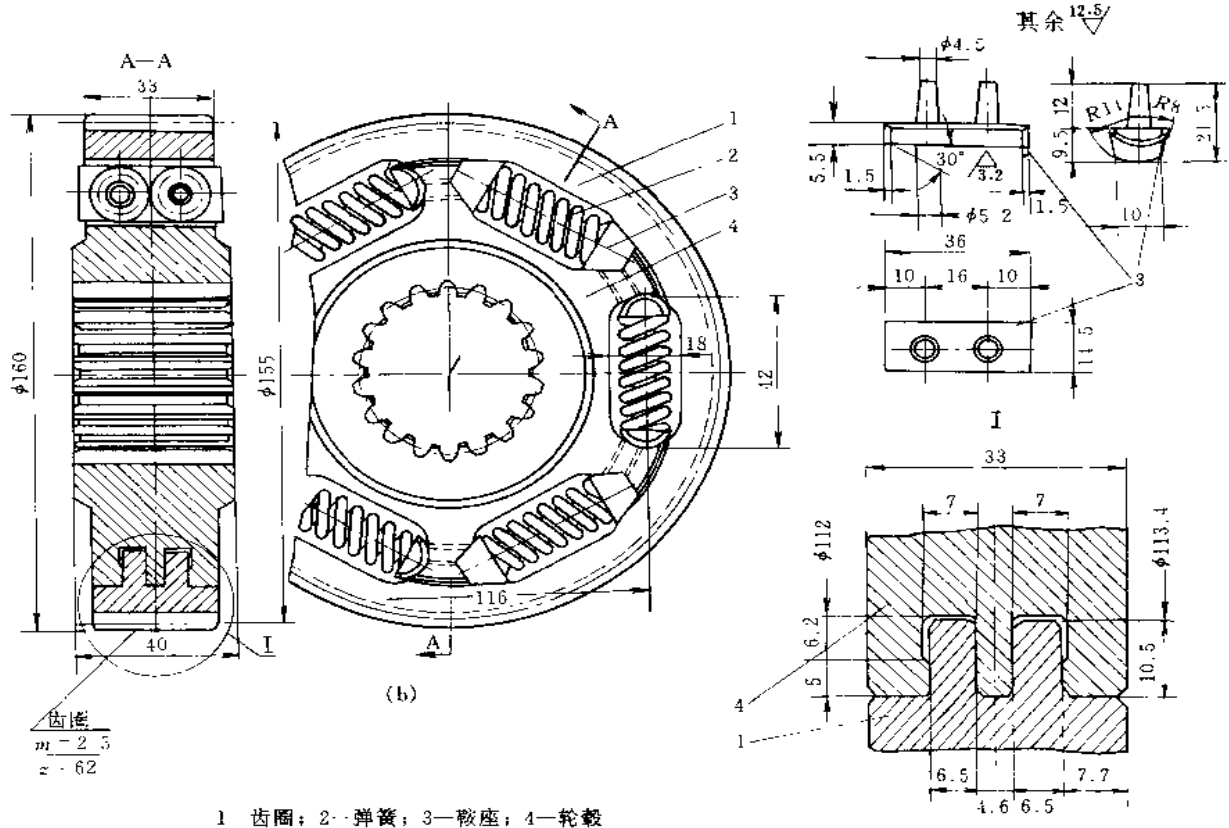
具有弹性元件的齿轮 (b) (c)
